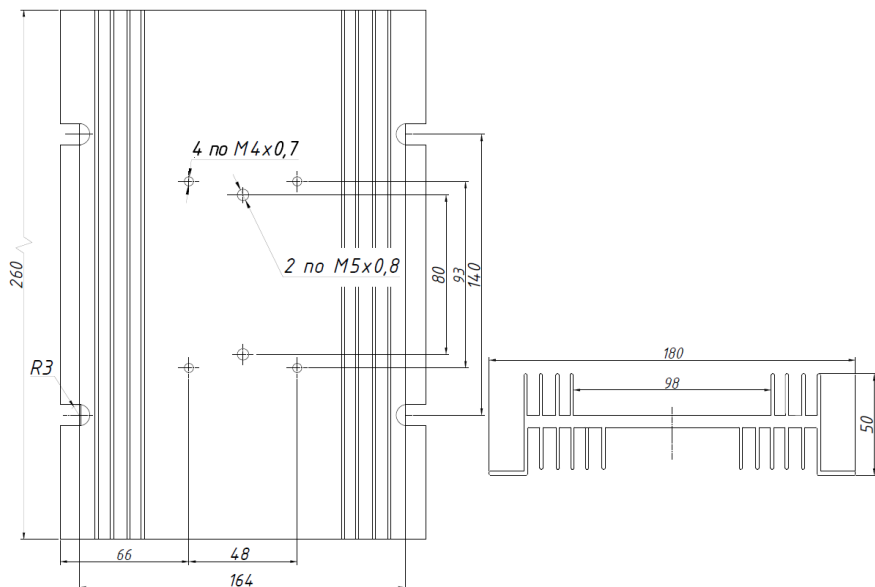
габаритные и установочные размеры радиатора PTP037
